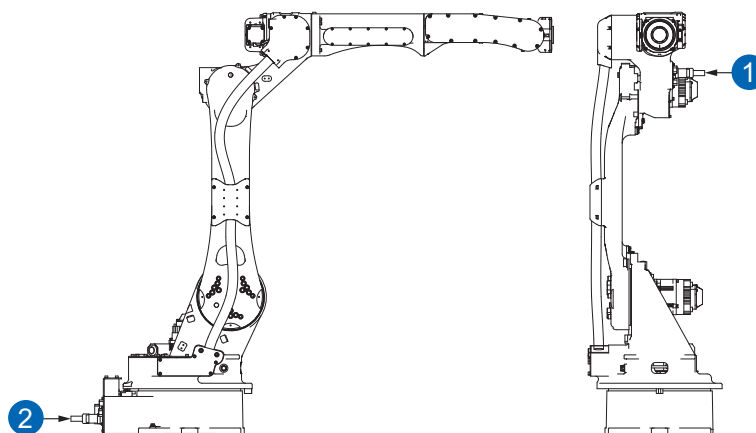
Gegenstecker für internen Kabelbaum für Anwender E/As (gerader Typ)
